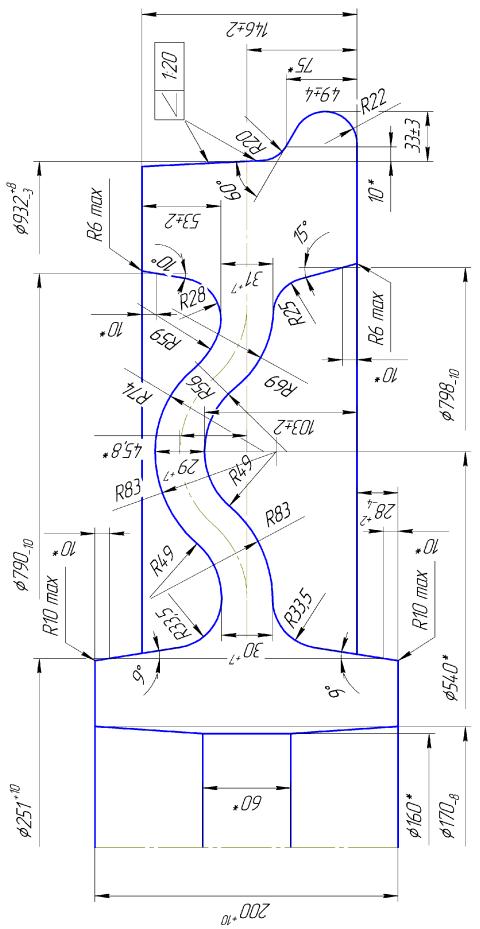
Колесо без механической обработки Ø 932 мм (после проката), конструкция ВА 004.
